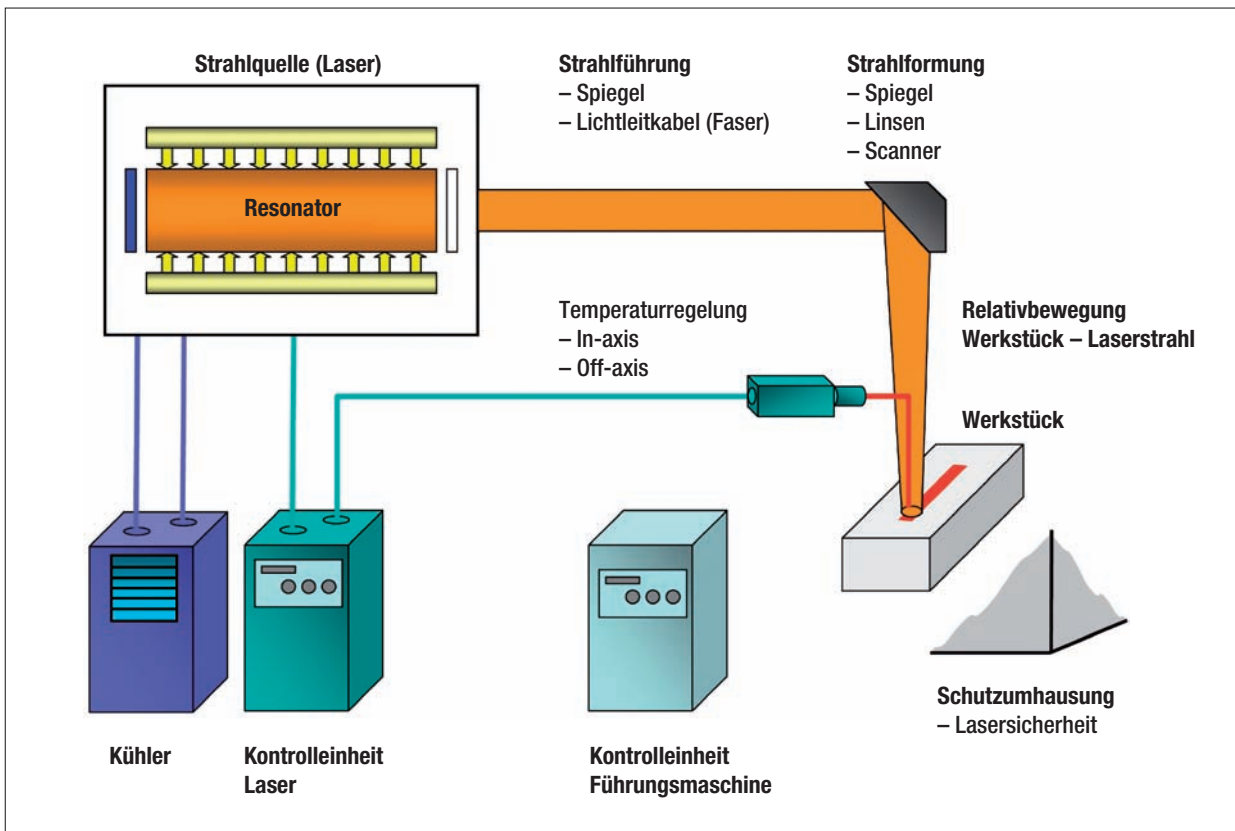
Prinzipieller Aufbau einer Laserstrahlhärtemaschine
